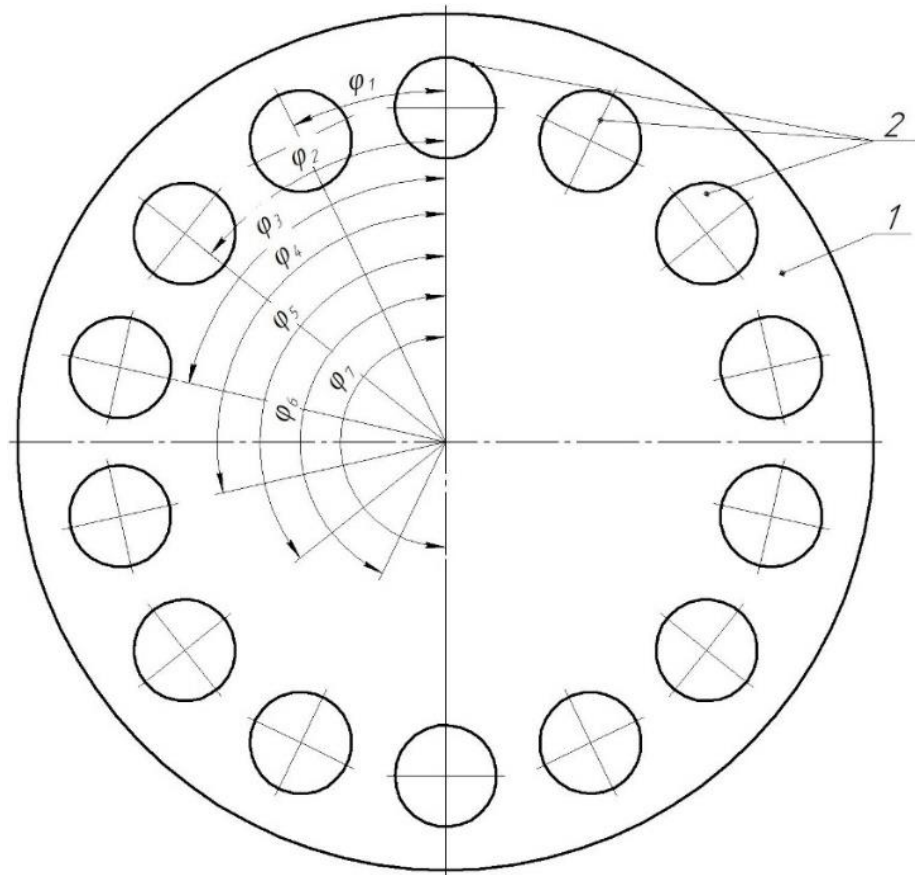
Кути повертання інструментального магазину: 1 - барабан; 2 – гнізда під інструменти
